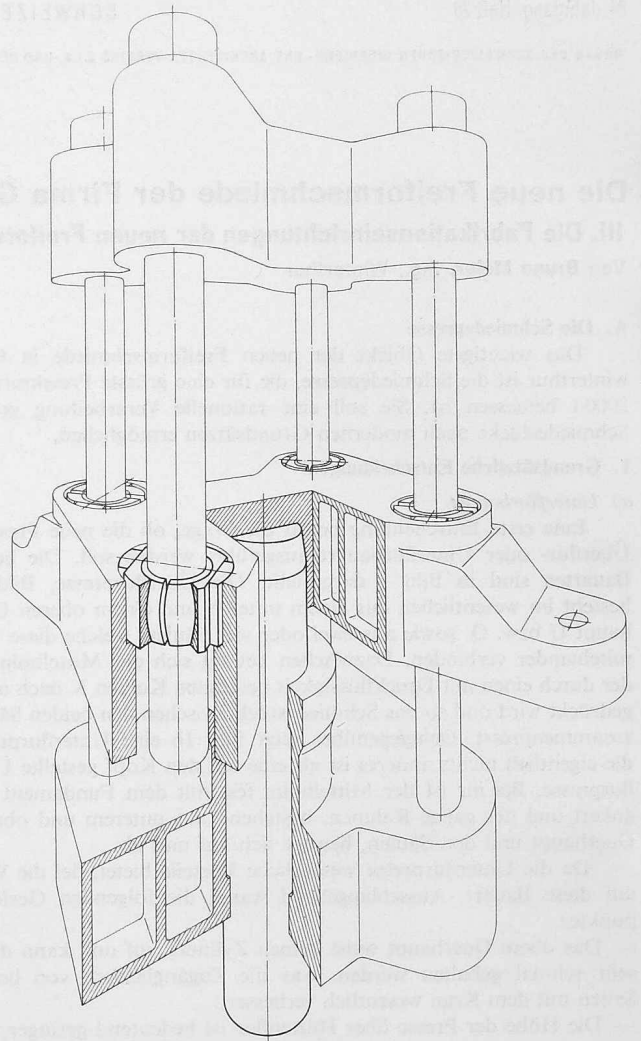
Führung einer Viersäulen-Schmiedepresse mit zentralem Führungsschaft
